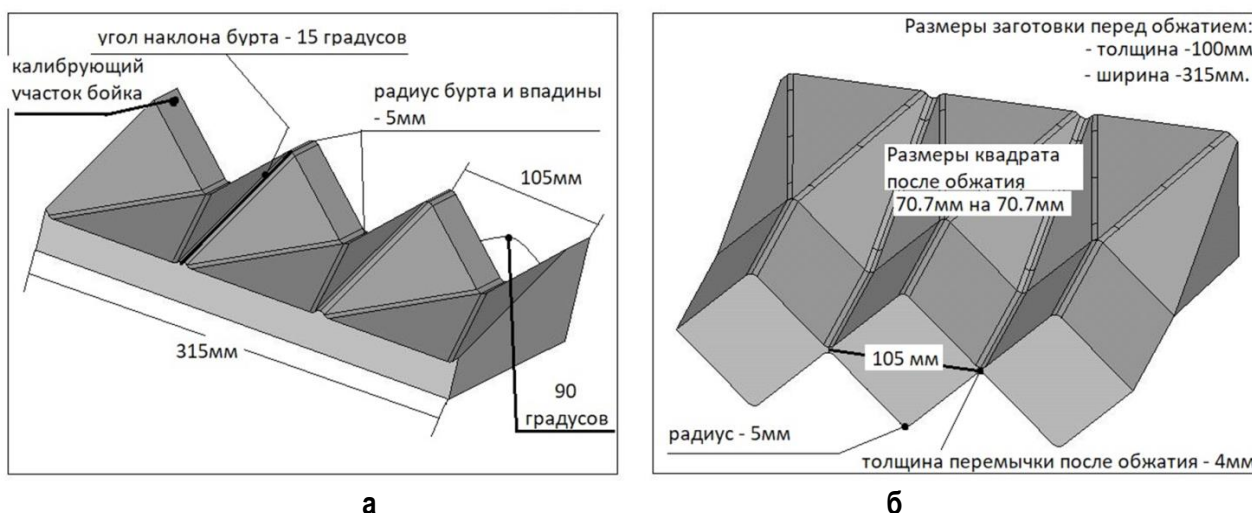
Изображение бойка (а) и трех сортовых заготовок (б) с размерами
